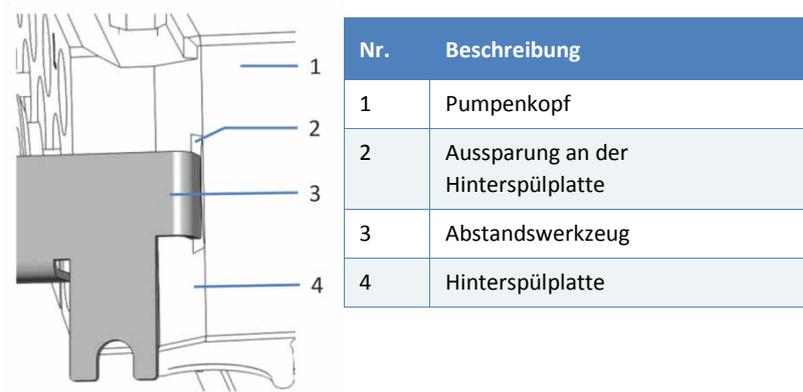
Entfernen der Hinterspülplatte mit dem Abstandswerkzeug
